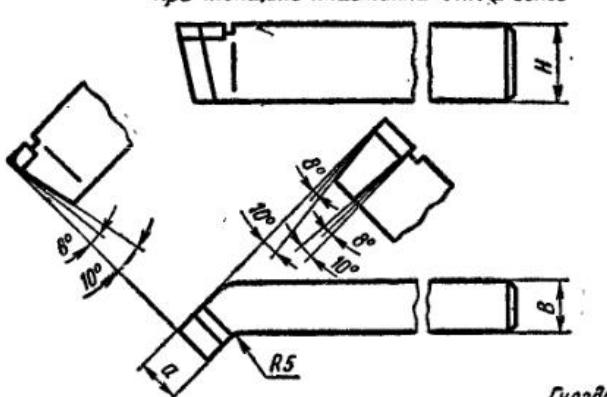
Конструкция резца с углом врезки пластиинки в стержень 10°
